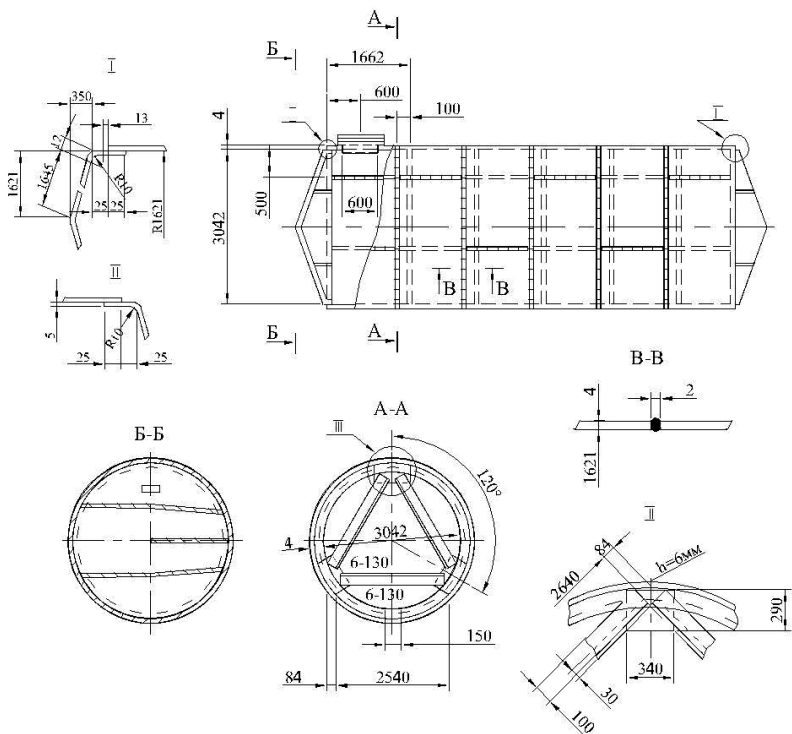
Горизонтальный цилиндрический резервуар с коническим дном
